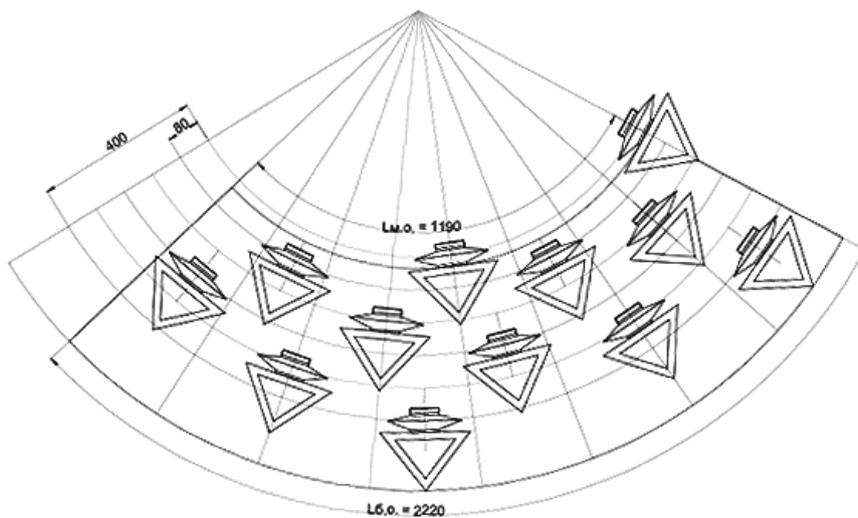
Схема набора дискового инструмента на развертке радиальной реверсивной коронки
